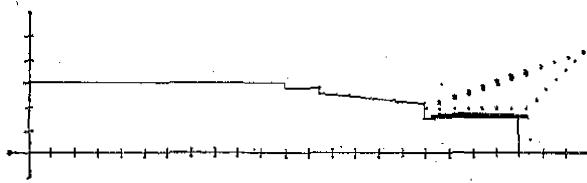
Контуры детали и заготовки и рассчитанной траектории инструментов в GTL-T
